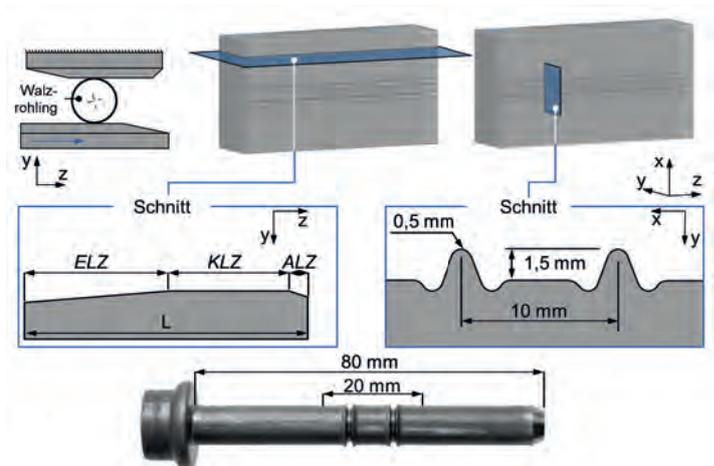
Prozessschema und verwendete Walzbacken (oben links), Profilgeometrien (mittig) und resultierendes, gewalztes Werkstück (unten)
